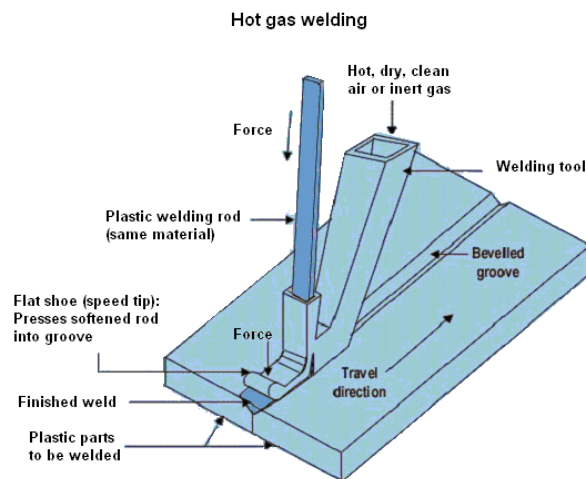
Rappresentazione schematica del processo “hot gas welding”
